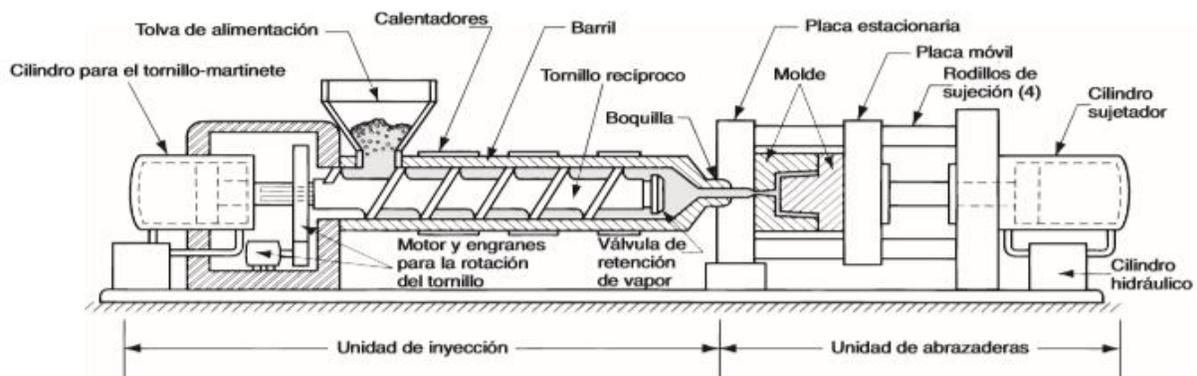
Diagrama de una máquina de moldeo por inyección.
